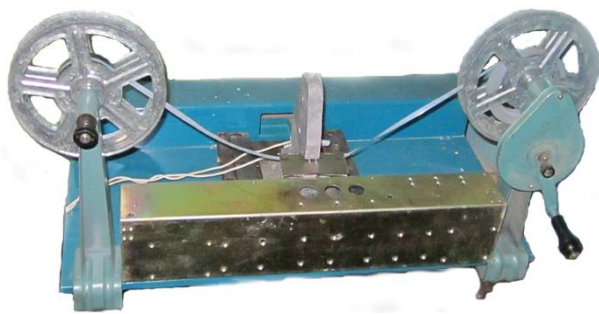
Экспериментальная установка для сварки лент из фторопластовых пленок
